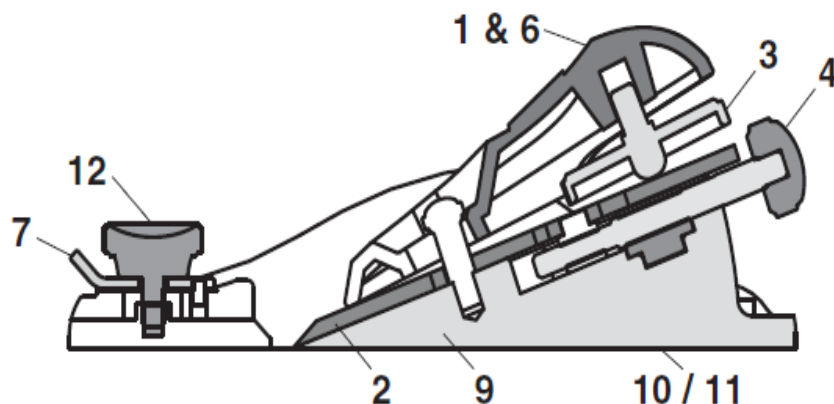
Vista de corte transversal del cepillo de bloque No. 9 1/2
